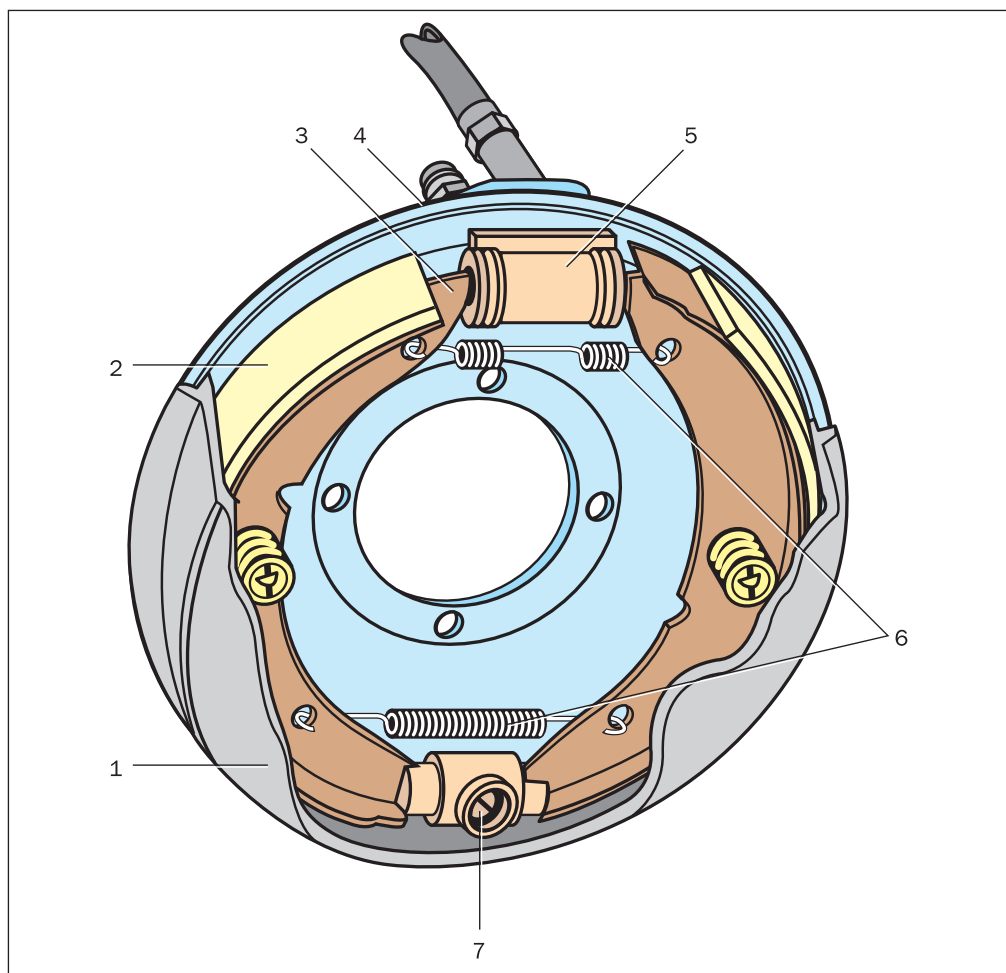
Барабанный механизм с равными приводными силами и односторонним расположением опор колодок: 1 — тормозной барабан; 2 — фрикционная накладка; 3 — колодка; 4 — тормозной щит; 5 — тормозной цилиндр; 6 — возвратные (стяжные) пружины; 7 — эксцентрик регулировки тормоза
